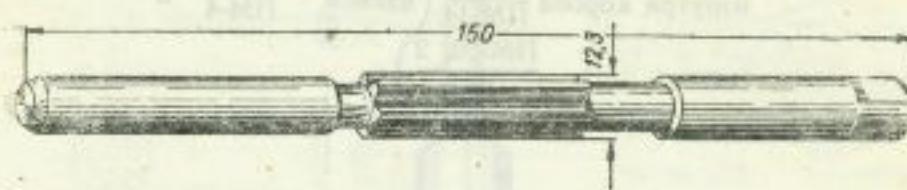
Развёртка с направлением для отверстий в ушках дна короба ВДП-И ПМ-4.
